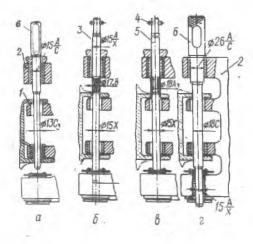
Последовательность переходов при разделке отверстий узла стика физеляжа с крылом: а предварительный контроль; б зенкерование; в развертивание; г окончательный контроль;
